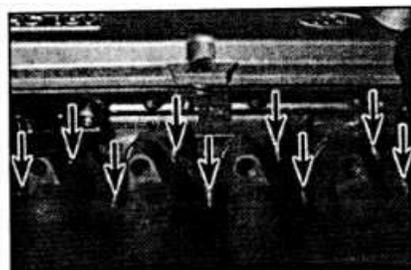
Е.14. Расположение гаек крепления выпускного коллектора на двигателях Zetec.
